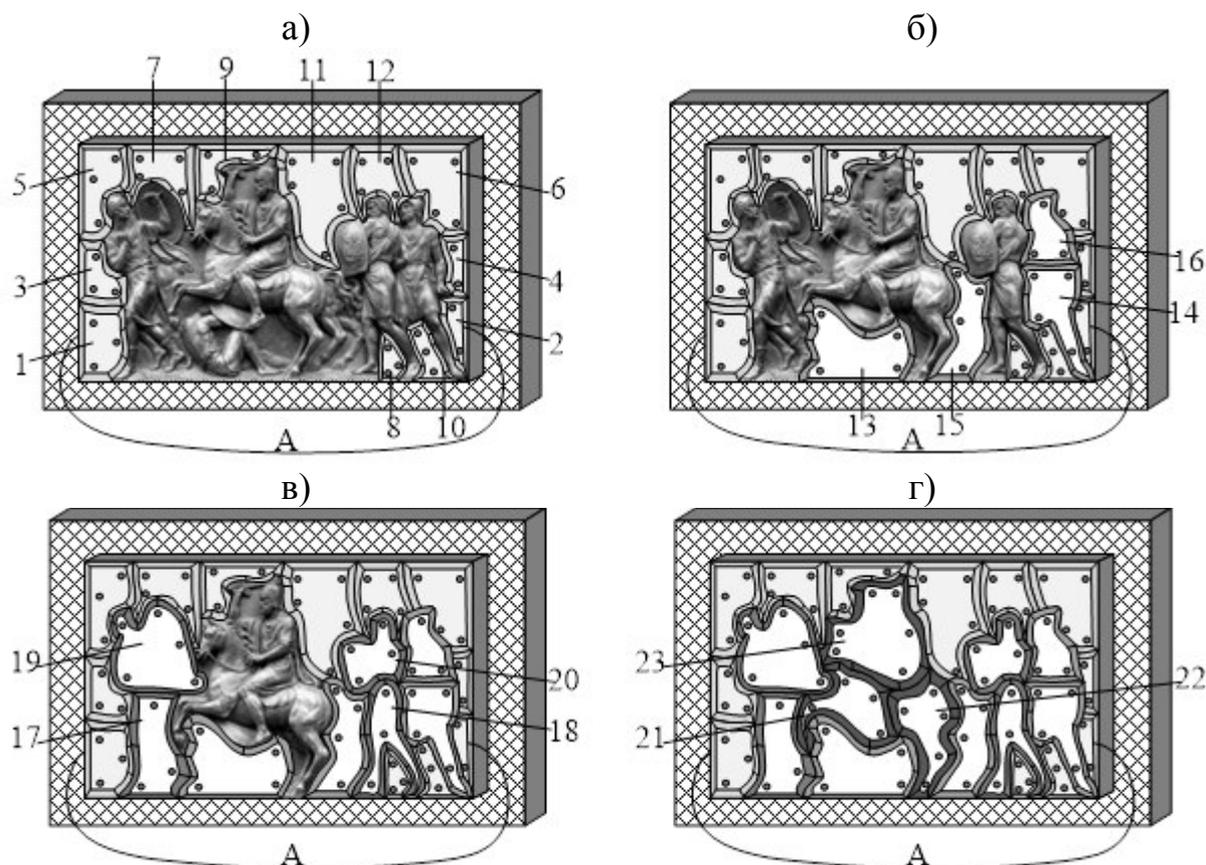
Снятие формы со сложного рельефа: а – формовка боковых кусков; б – формовка внутренних кусков; в – формовка более уровневых кусков; г – формовка самой выступающей части рельефа; 1–23 – последовательность заложения кусков; А – скоба
